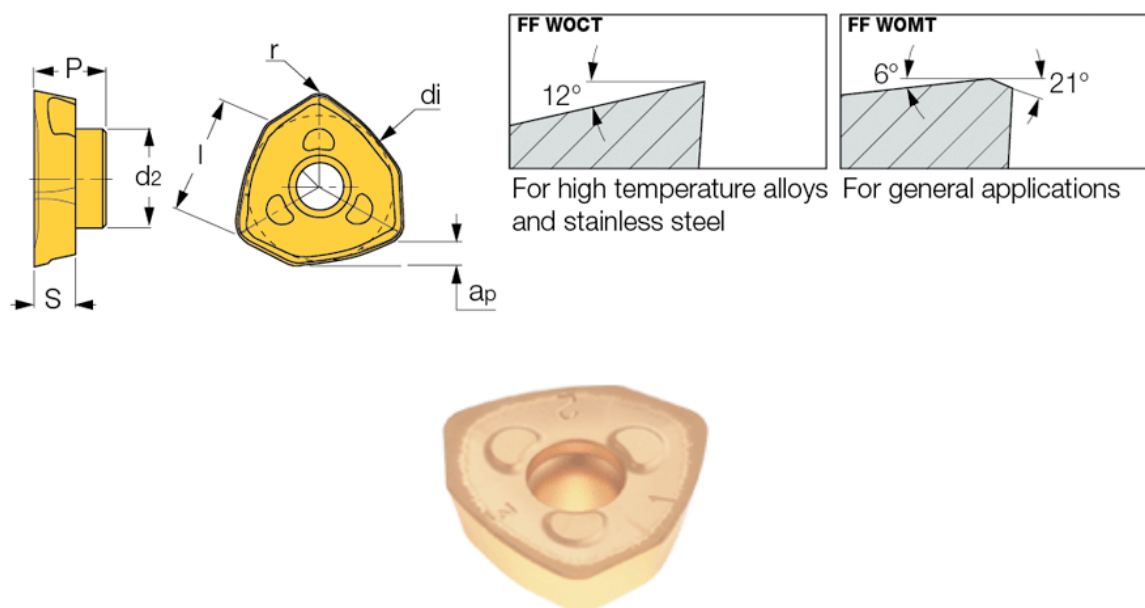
Fréza FF FWXD050-06-22-05 [19]
